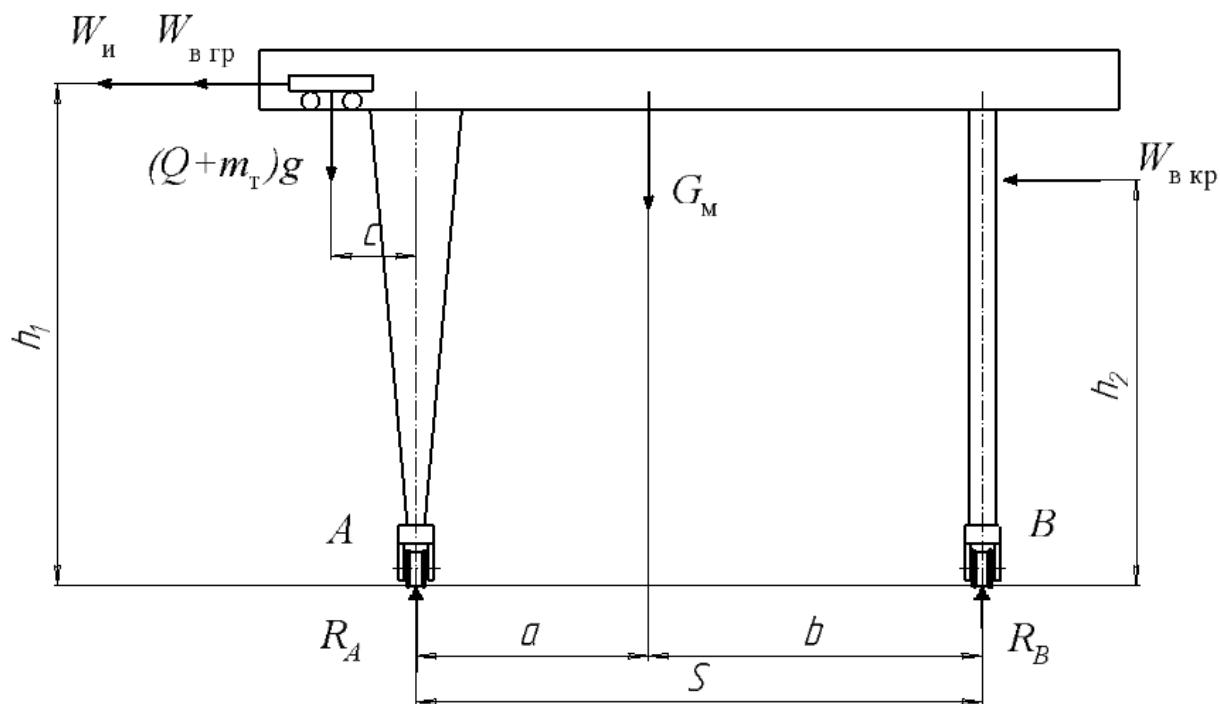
Расчетная схема к определению нагрузок на опоры козлового крана
